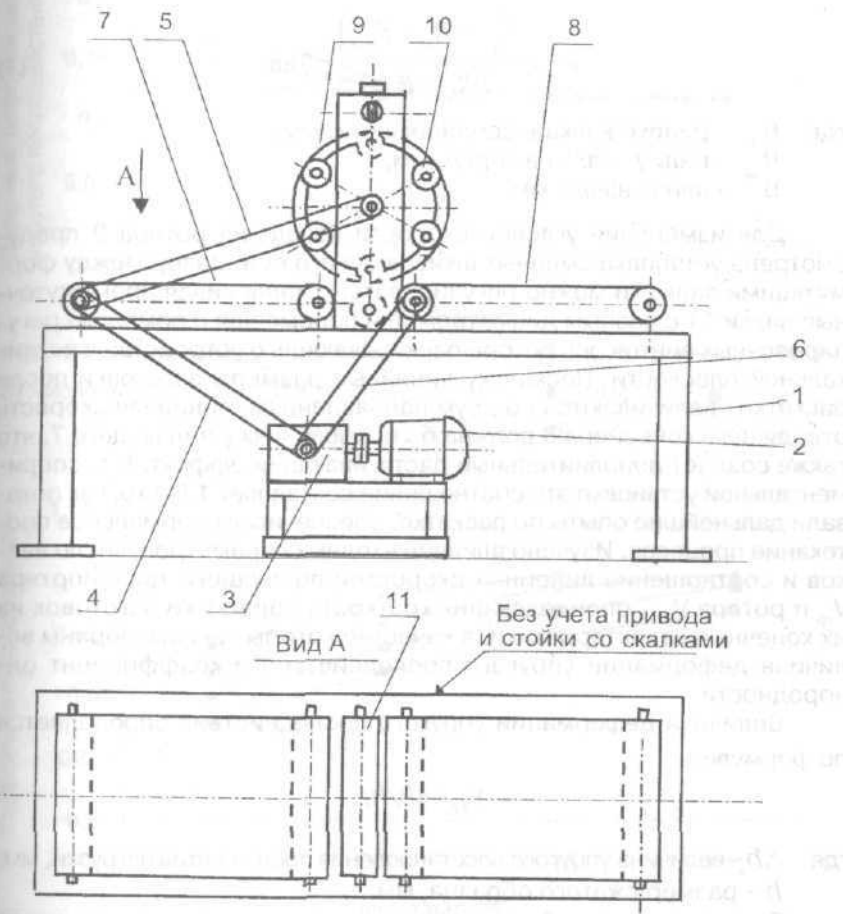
Схема машины для раскатки слоеных мучных изделий: 1 - несущая рама; 2 - электродвигатель; 3 - редуктор; 4, 5, 6 - ременные передачи; 7, 8 - ленточные транспортеры; 9 - раскатывающее устройство; 10 - валки; 11 - цилиндрический валик
